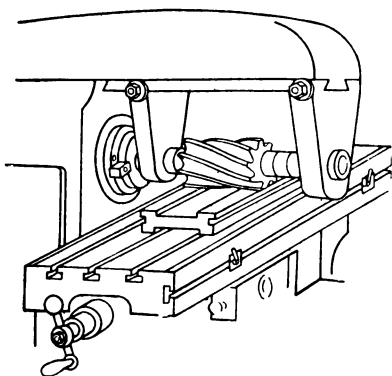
Постановка добавочного подвешного подшипника хобота станка
